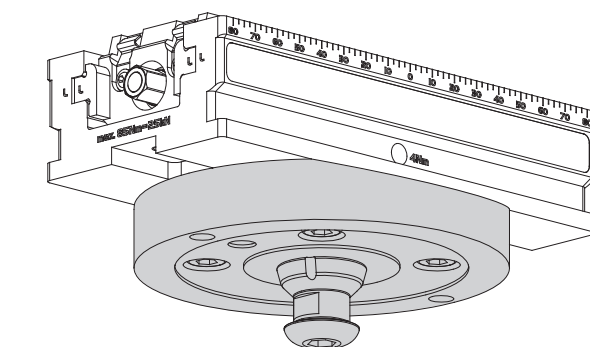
Menghină cu fixare centrică cu GARANT ZeroClamp
